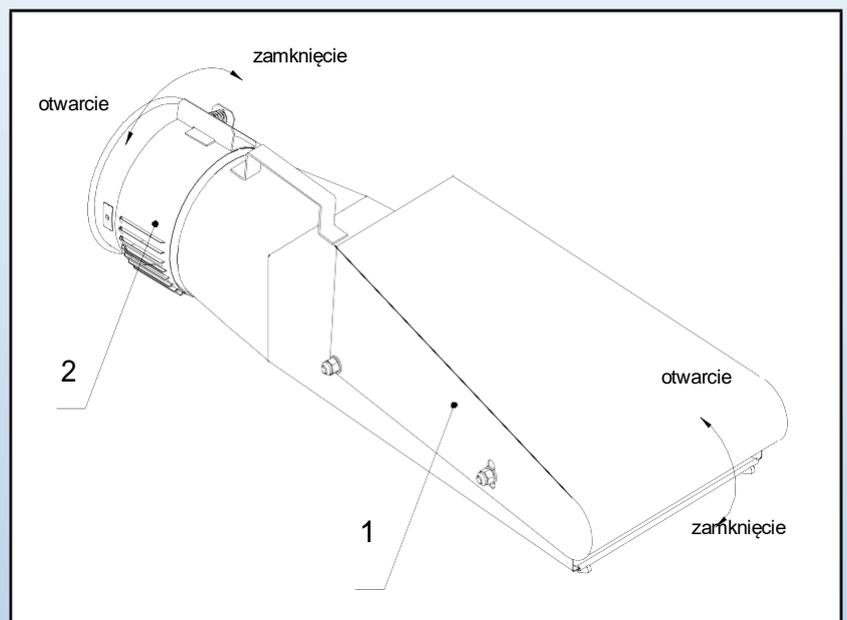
Boquilla (1 - Cubierta; 2 - Apertura)
